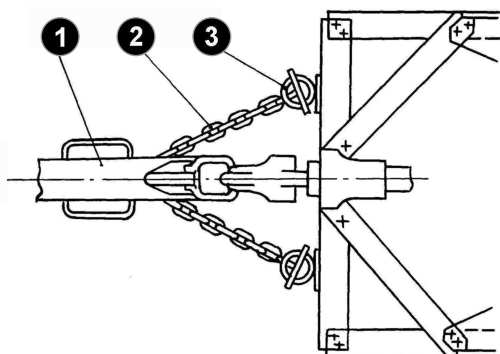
Схема крепления компрессорной станции предохранительными цепями
